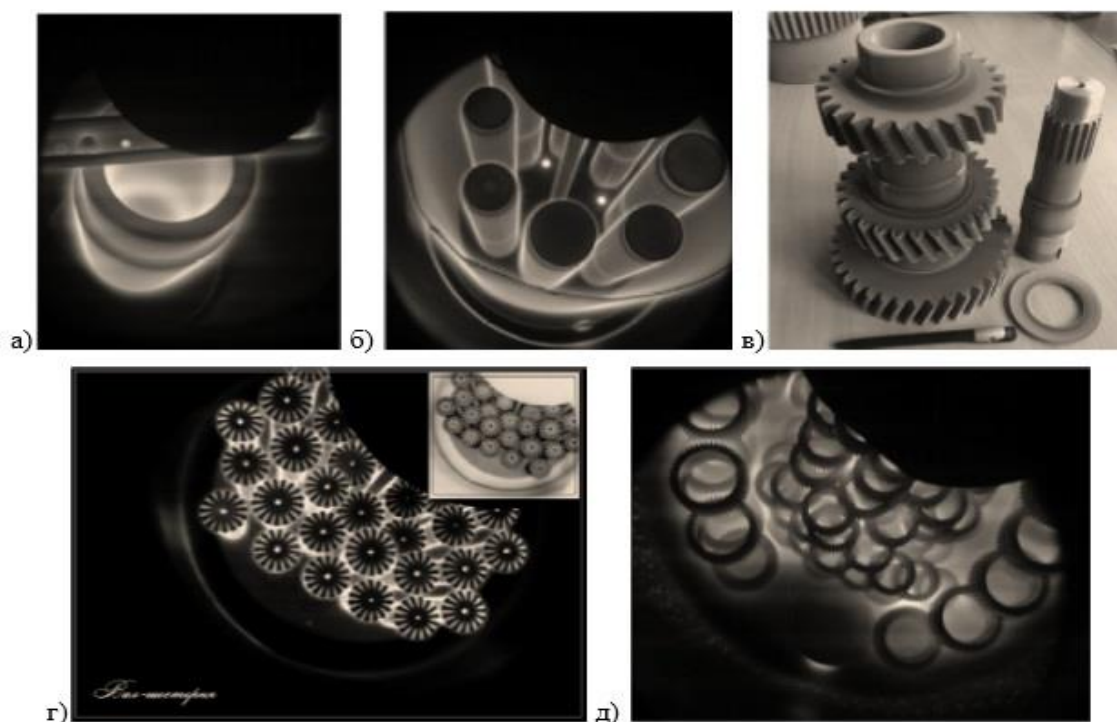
Процес ПТА для деяких деталей: а) гільза; б) шпindelь; в) шестерня і вал-шестерня; г) вал-шестерня; д) зубчасті колеса.
